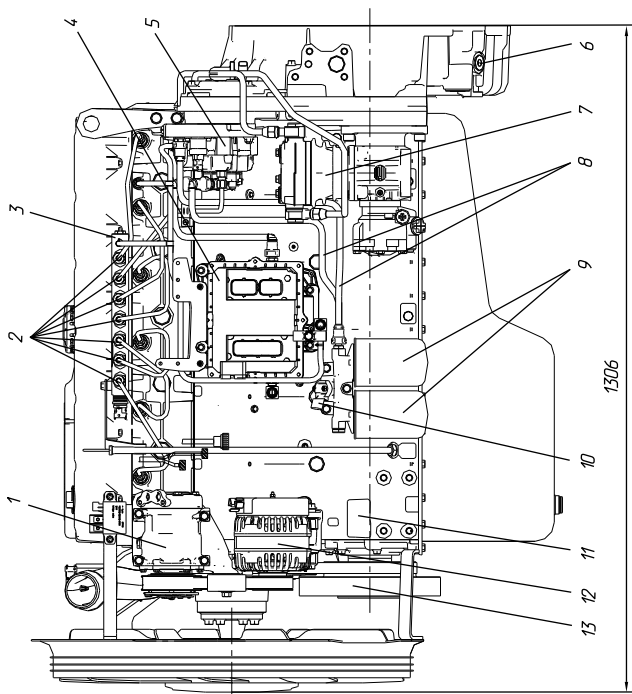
Габаритные размеры, расположение агрегатов и узлов двигателя ЯМЗ-Э5367 (вид слева):
